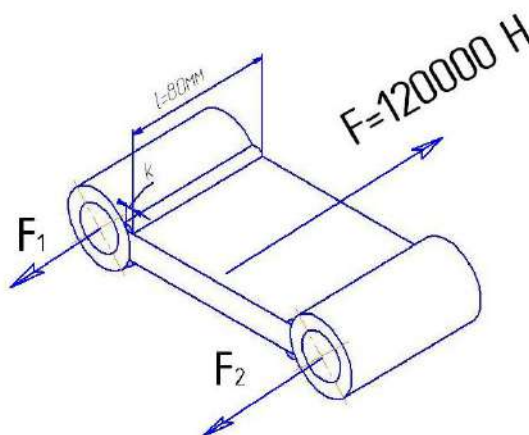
Сварные соединения втулок траверсы
